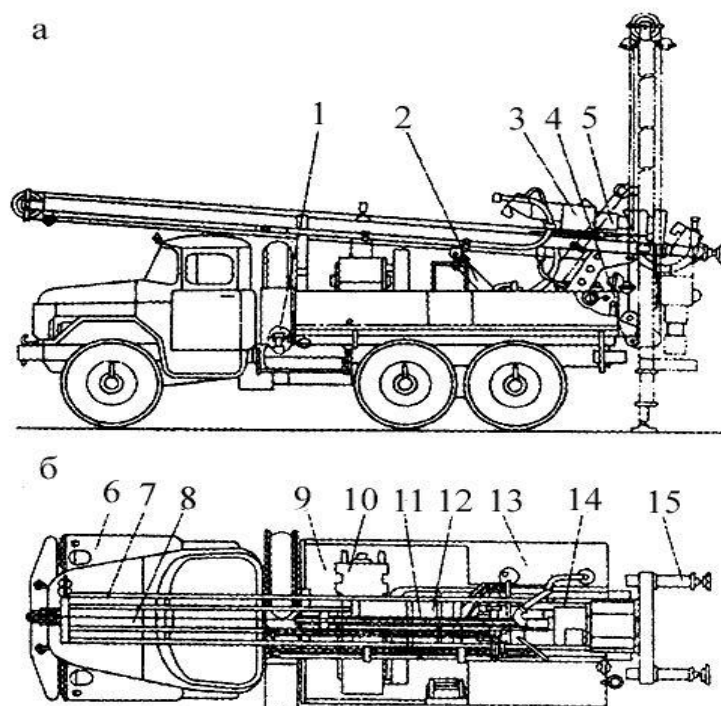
Схема буровой установки УРБ-2А-2: а – вид сбоку; б – вид сверху; 1 – коробка отбора мощности; 2 – цилиндр подъема мачты; 3 – вращатель; 4 – пульт управления; 5 – элеватор для труб и патрон для шнеков; 6 – автомобиль; 7 – мачта; 8 – талевая система; 9 – рама; 10 – установки бурового насоса и компрессора; 11 – гидродомкрат подачи; 12 – раздаточная коробка; 13 – обвязка гидросистемы; 14 – каретка; 15 – опорный домкрат.
